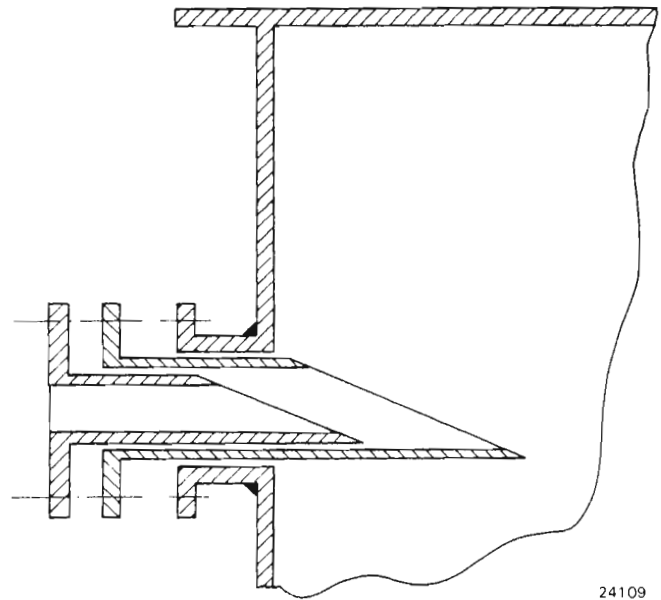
Conjunto de tubos de extracción interior y exterior removibles
